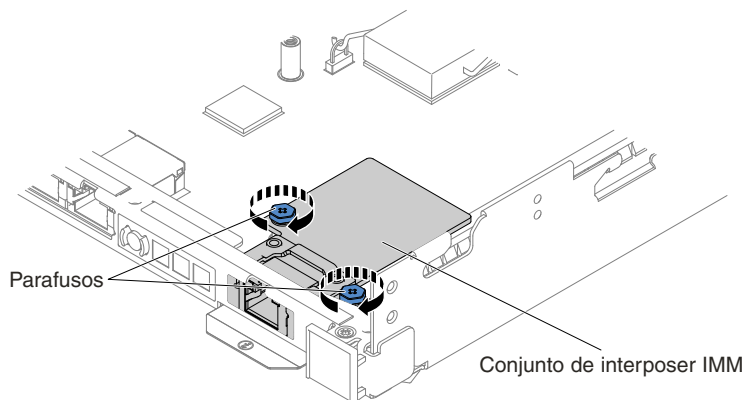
Instalação do conjunto de cabo adaptador de IMM
